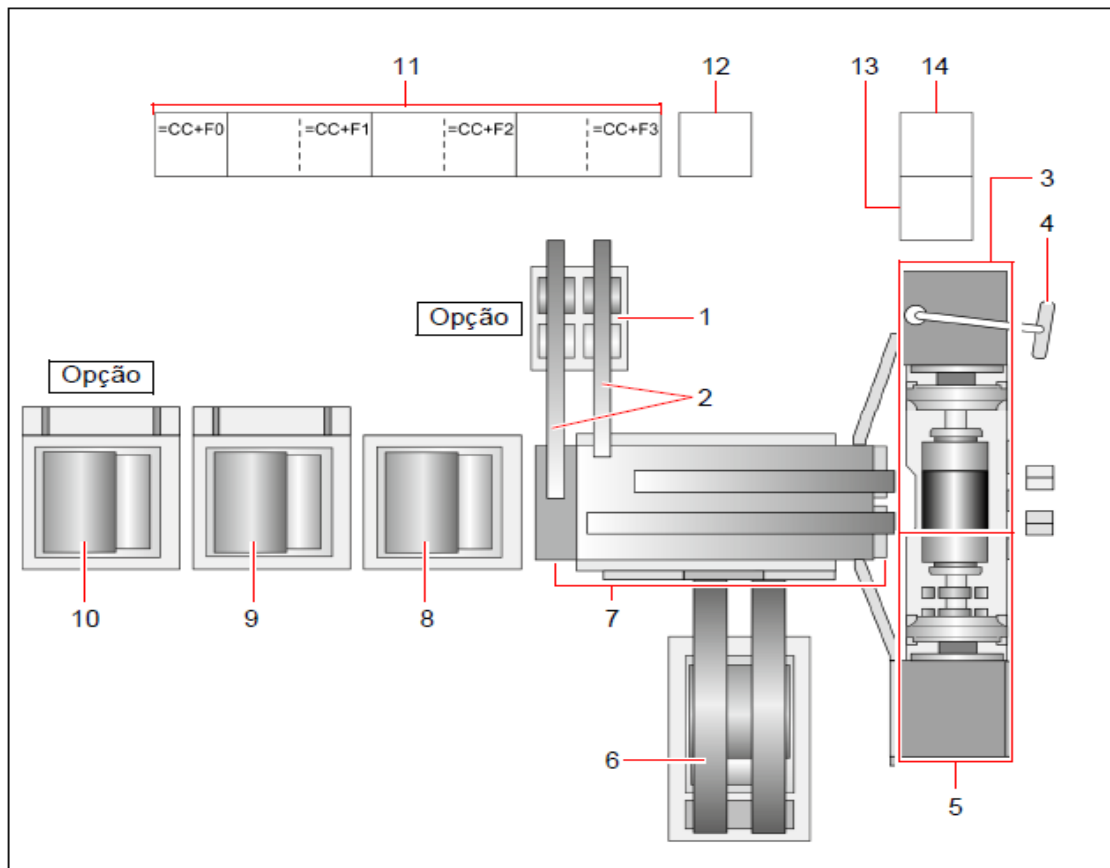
Desenho representativo das principais peças que constituem a KM 7 (Machinery, 2014a).
